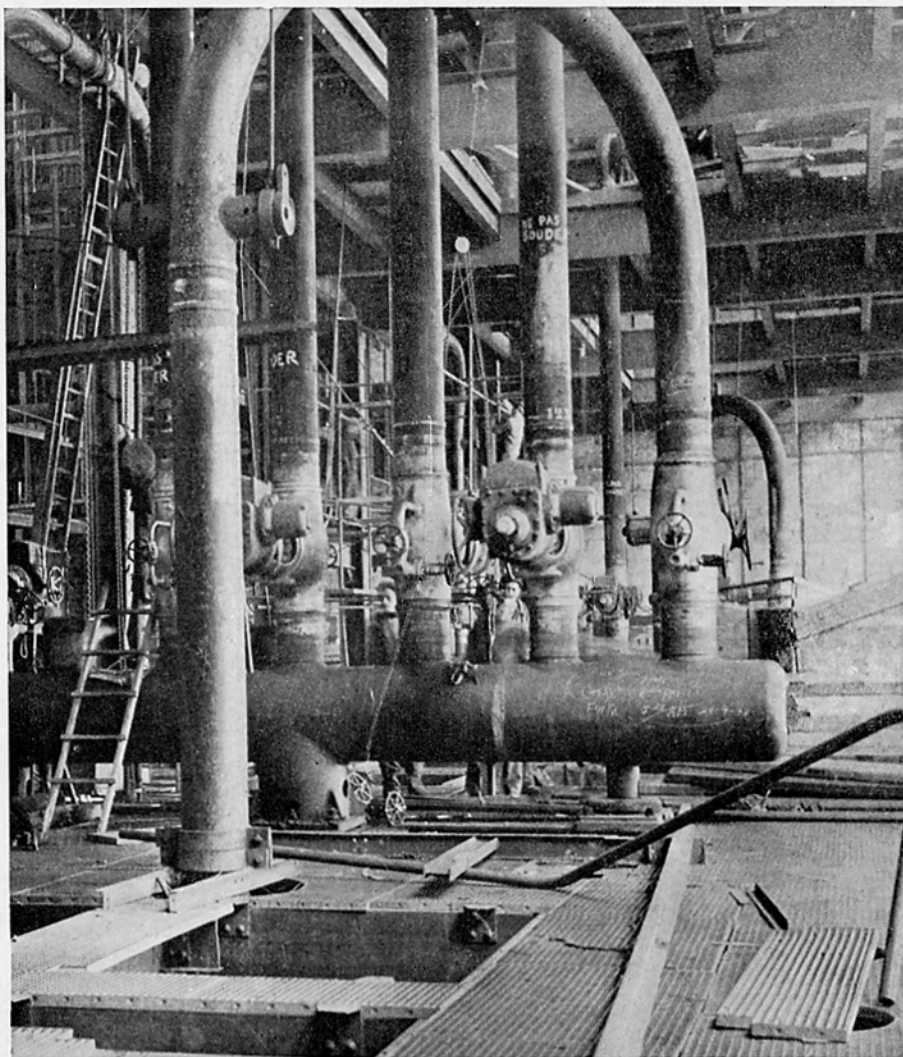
Vue prise pendant l'exécution d'une soudure. On remarque la disposition des enroulements de chauffage et des couples de contrôle de la température.
